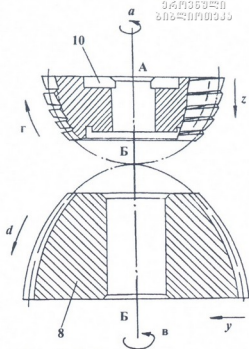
Схема нарезания эллипсоидного зубчатого колеса
